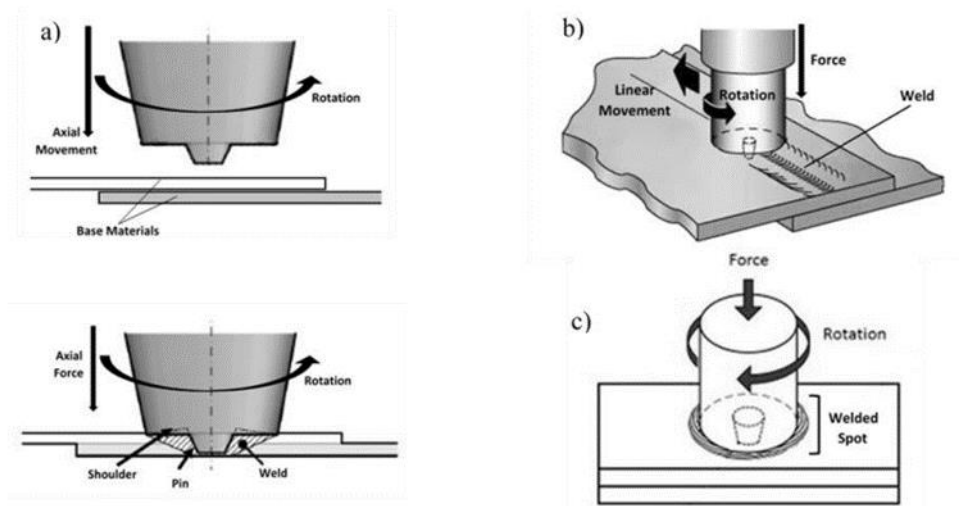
a) Movimento axial e rotativo da ferramenta de soldadura b) Friction Stir Welding (FSW) c) Friction Stir Spot Welding (FSSW).
